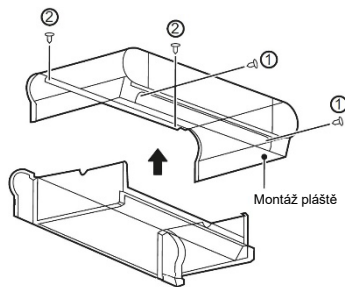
Vyjmutí filtru a krytu horního a šroubů motoru
